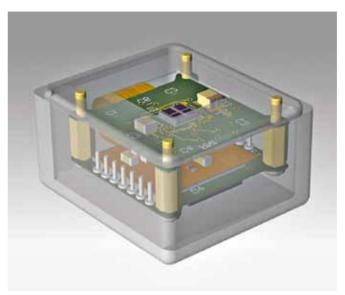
Гибко-жесткая плата в окне трехмерного вида Xpedition в корпусе (корпусу задано значение прозрачности в 60%, что позволяет видеть плату и корпус одновременно)
